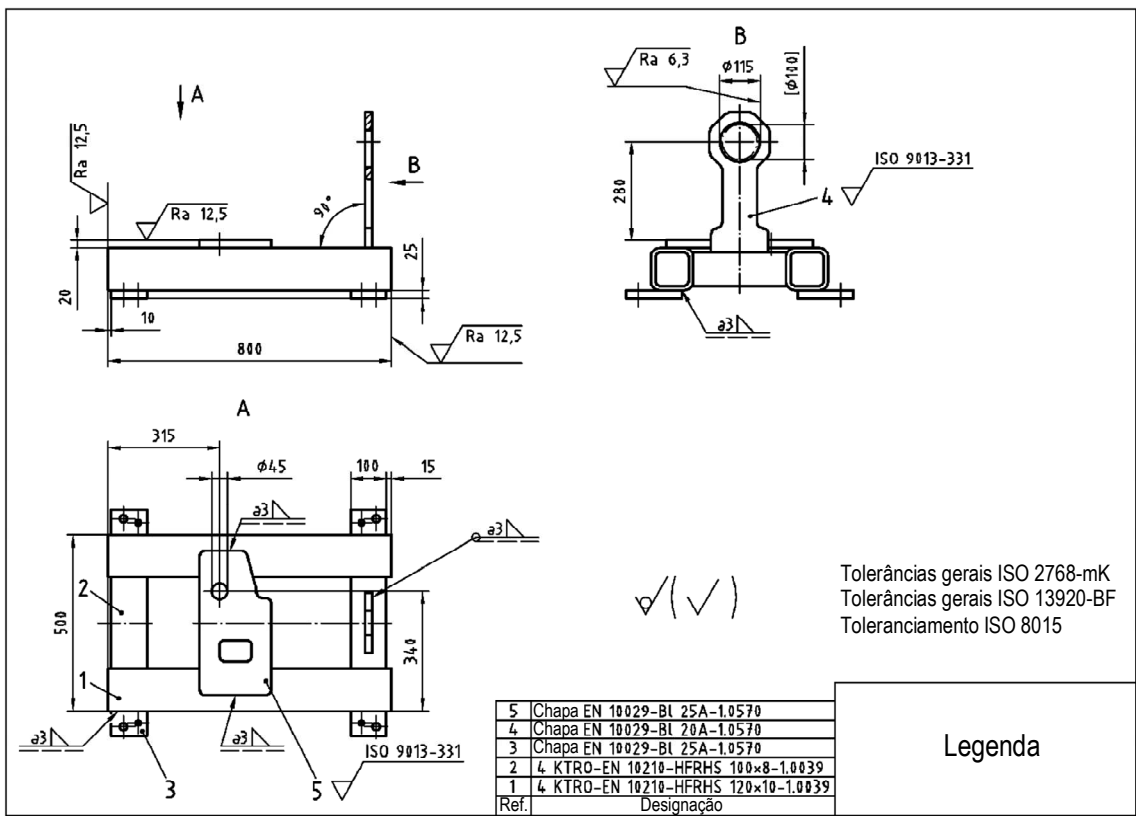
Exemplo de um desenho de uma estrutura soldada. Adaptado da norma DIN 30630
